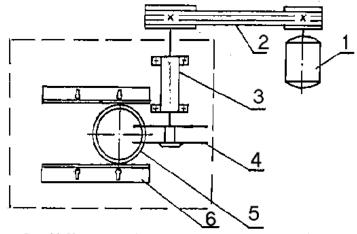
Устройство для разрезания поперечного шва банки: 1 – электродвигатель; 2 – клиноременная передача; 3 – опора; 4 – дисковые пилы; 5 – разрезаемая банка; 6 – планка
